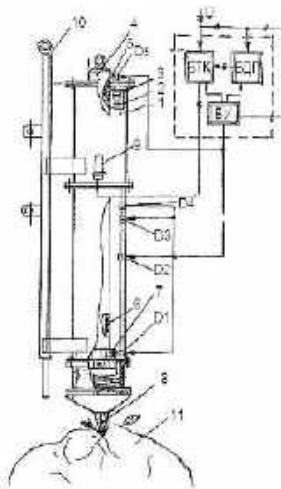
Молот (М-КЛАД) для руйнування негабаритного матеріалу: 1 – корпус молота; 2 – статор ЛАД; 3 – обмотка статора ЛАД; 4 – бігун (ударник); 5 – сердечник бігуна; 6 – обмотка (кільце) бігуна; 7 – п’ята бігуна (ударника); 8 – робочий інструмент; 9 – кабельний ввід; 10 – направляюча; 11 – негабаритний матеріал; D1-D5
